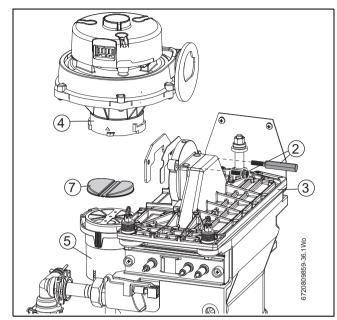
Démontage du ventilateur - exemple version 42 kW
